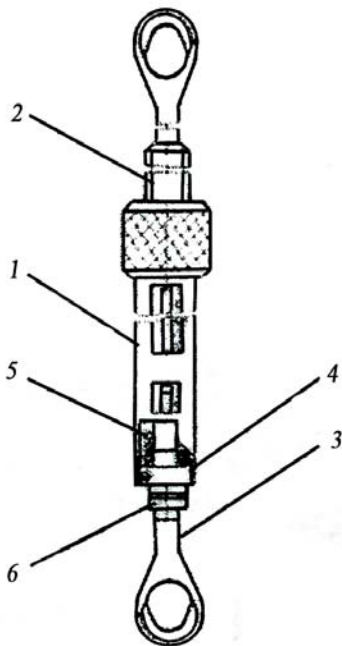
Прилад КИ-6296 для перевірки натягу гусеничного ланцюга: 1 – корпус; 2 – захват верхній; 3 – захват нижній; 4 – пробка; 5 – пружина; 6 – гайка.
